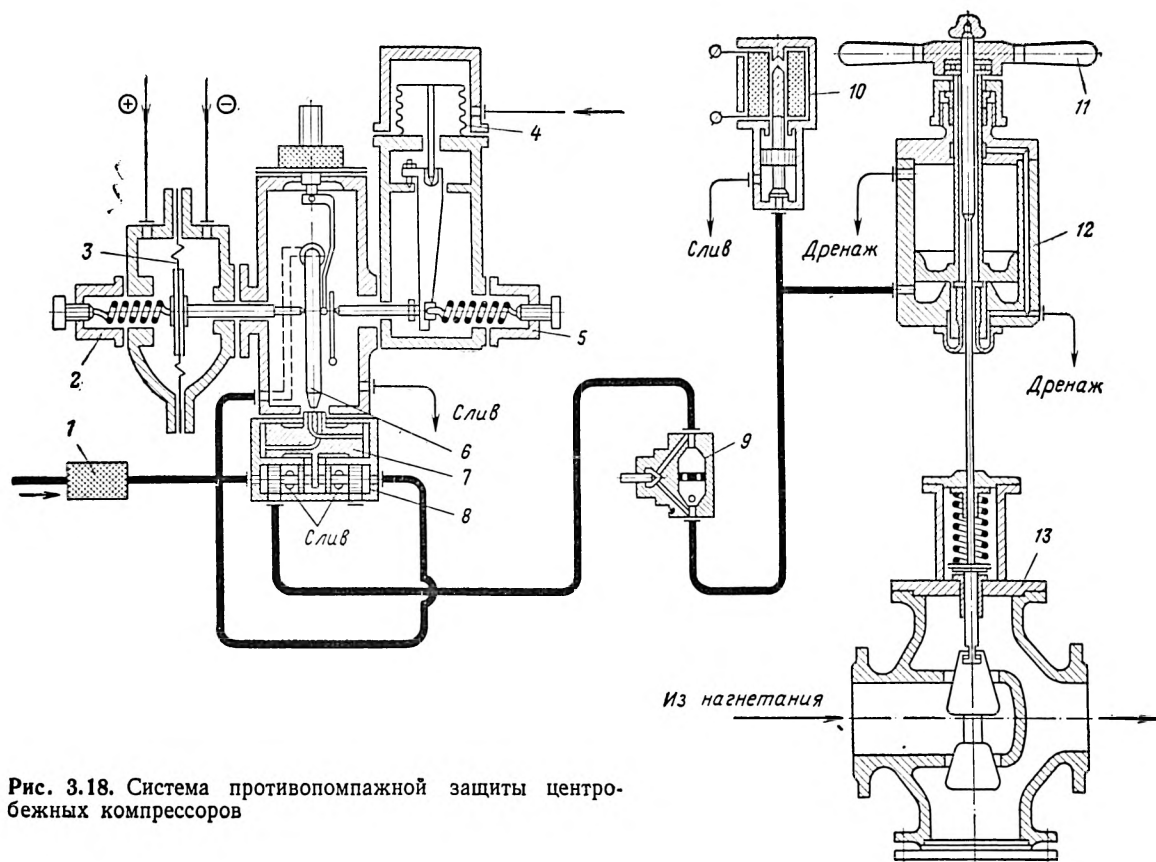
Система противопомпжной защиты центробежных компрессоров
